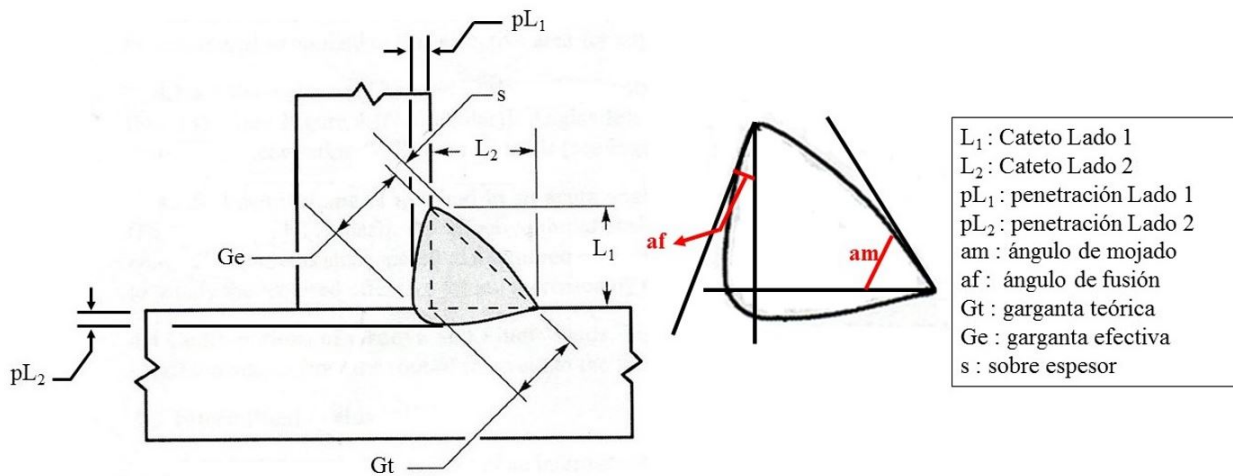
Parámetros de una soldadura de filete. Fuente imagen: SCielo.
